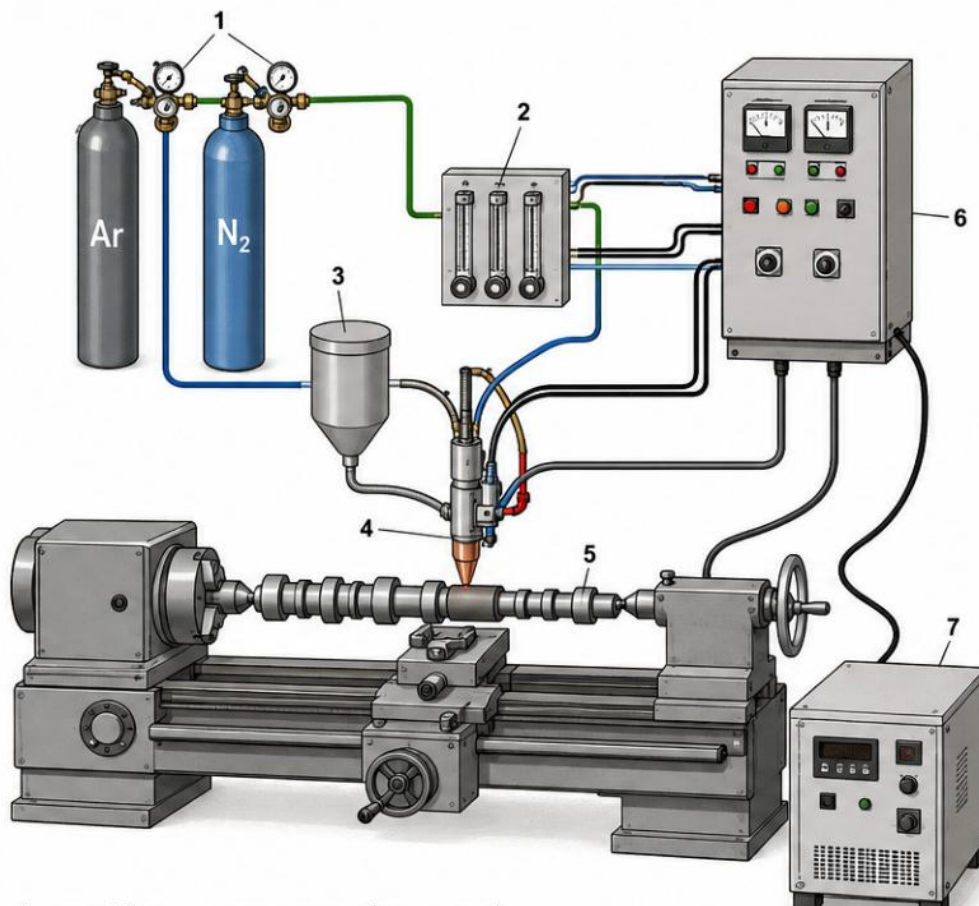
Схема установки для плазмового наплавлення розподільного вала:
